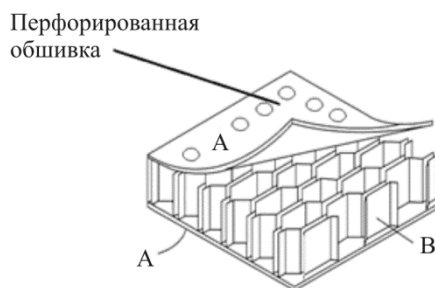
Звукопоглощающая конструкция: 1 – верхняя и нижняя обшивки; 2 – сотовый наполнитель
